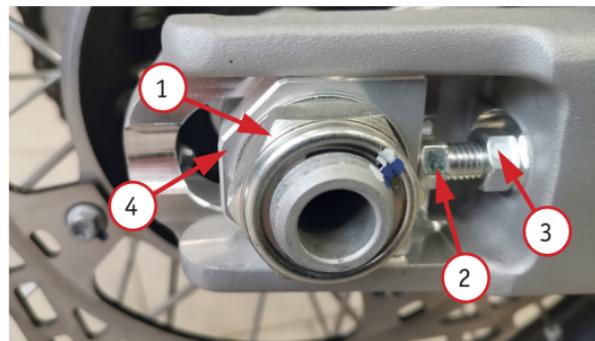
Регулировка натяжения цепи: 1 – гайка оси колеса; 2 – регулировочный болт; 3 – стопорная гайка; 4 – кронштейн натяжителя
